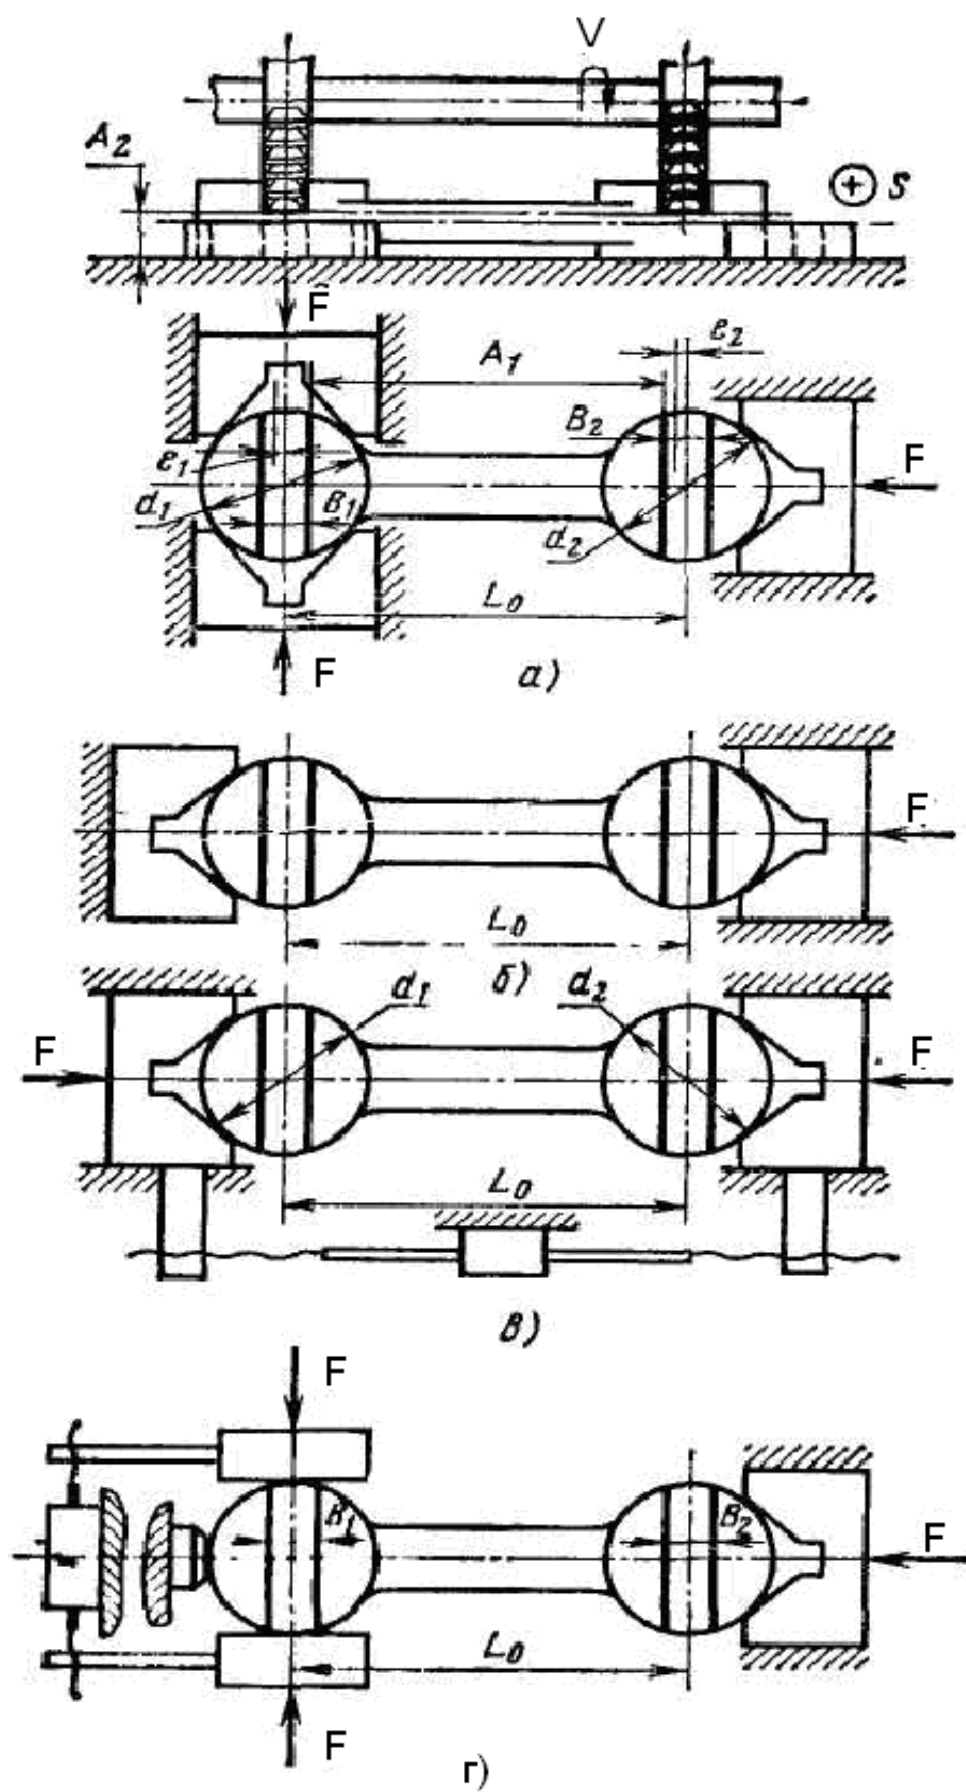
Схеми обробки пазів в головках шатуна (до задачі 1.15.)
